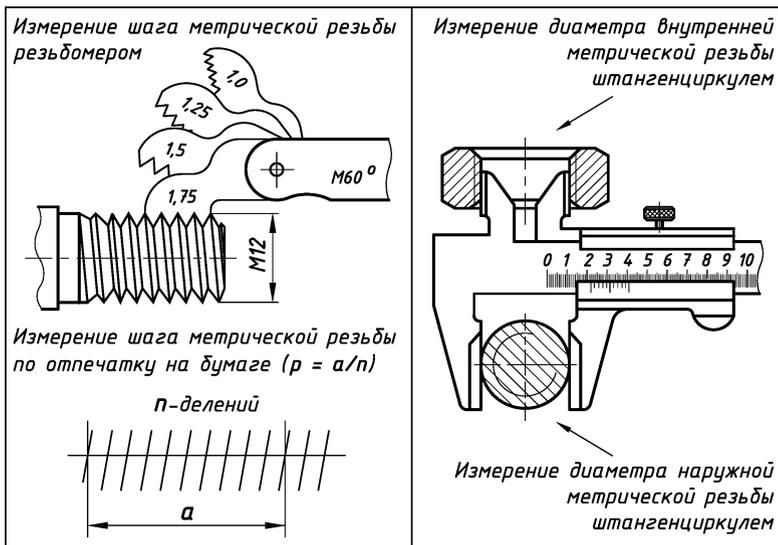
Определение параметров резьбы метрической цилиндрической
